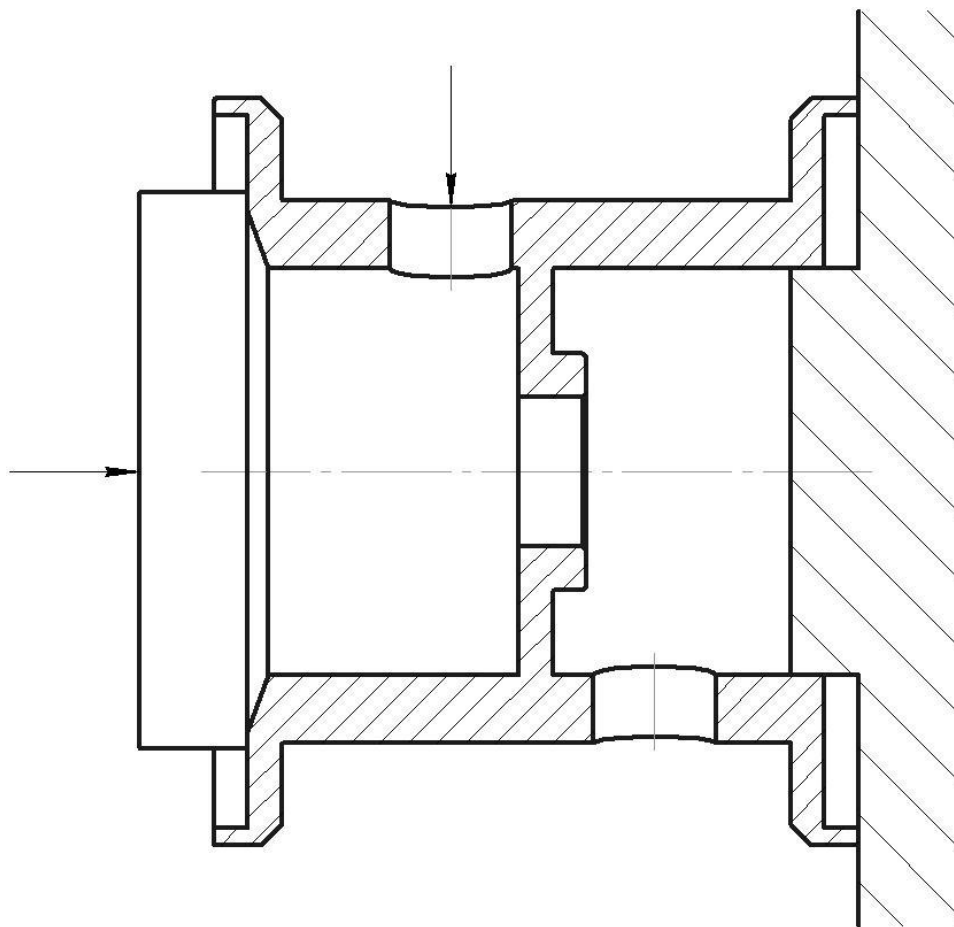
Заготовка с указанием возможных мест приложения усилий
